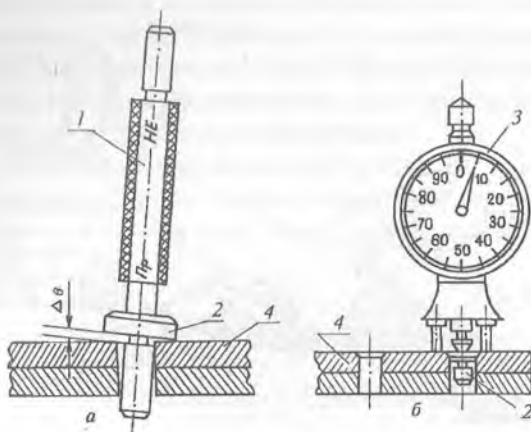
Контроль отверстия и зенкованного гнезда под заклепку: 1 — калибр-пробка; 2 — калибр-заклепка; 3 — индикатор; 4 — соединяемые детали
